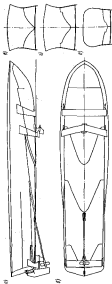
Схема крылового катера «Волга» и детали конструкции: а — план корпуса; б — вид на левый; в — вид на правый; г — вид на носовой; д — вид на кормовой; е — вид на корпус крыла.
